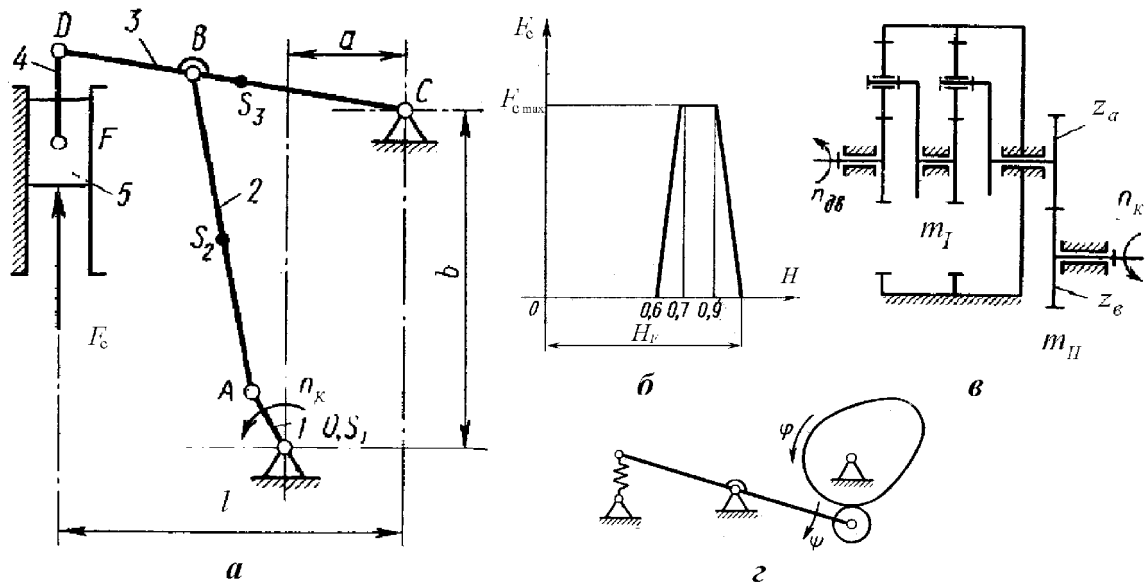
На схеме: а-рычажный механизм перемещения ползуна с пуансоном; б-график изменения усилия вытяжки; в- схема привода рычажного механизма; г-схема кулачкового механизма выталкивателя готовой детали
